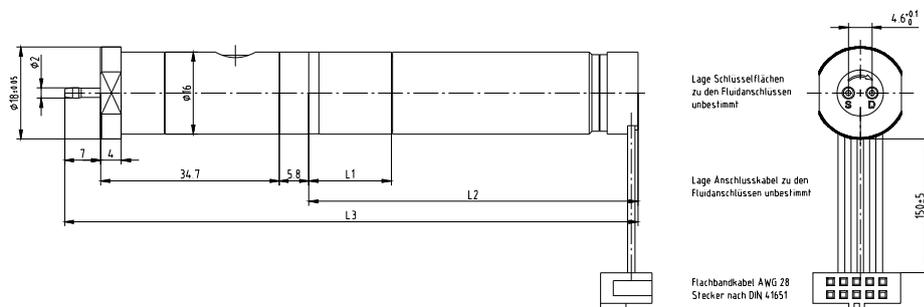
Abmessungen Mikrozahlringpumpen mzr-2542 und mzr-2942 mit Getriebemodul
